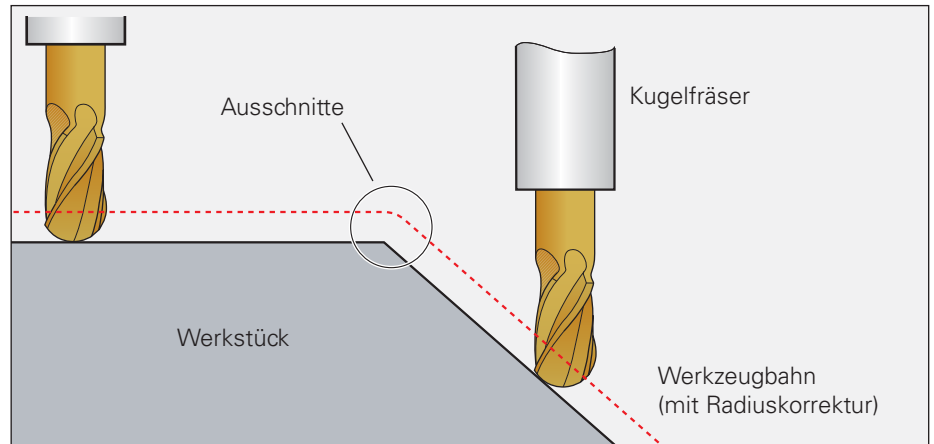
TCP-Werkzeugbahn für einen Kugelfräser
